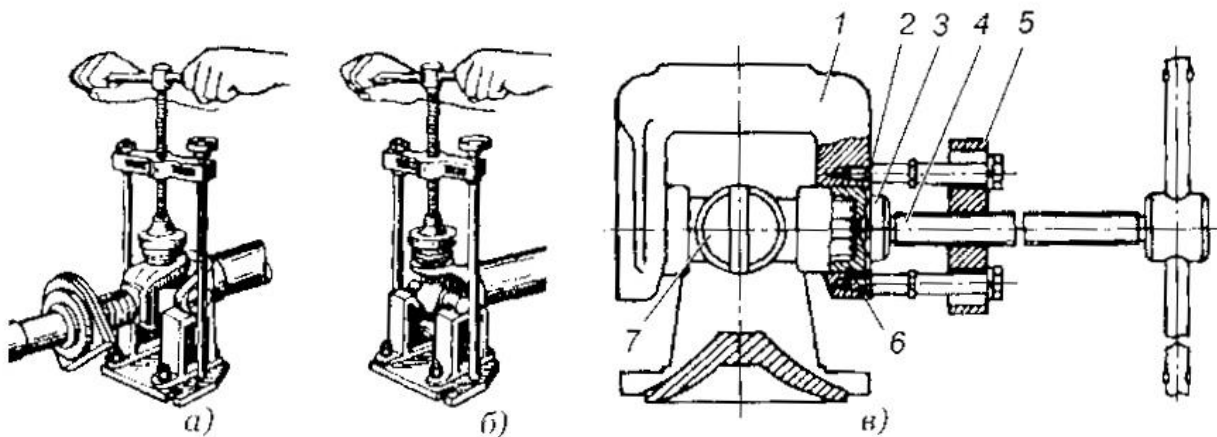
Розбирання карданного шарніра за допомогою універсального знімача: а) - випресування підшипників із ковзної вилки; б) - випресування підшипників з вилки карданного валу; в) - розбирання карданного валу трактора
